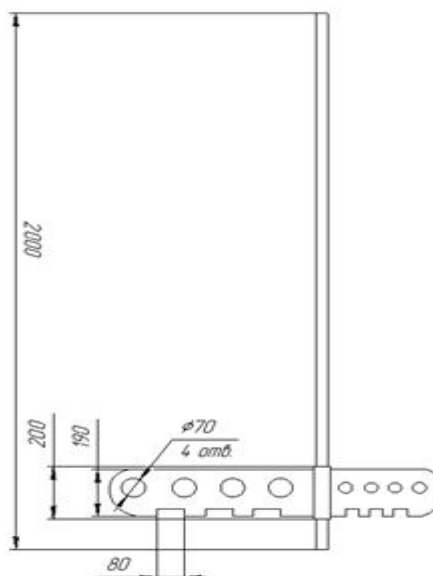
Перемешивающее устройство для резервуара В2-ОМВ-2,5
